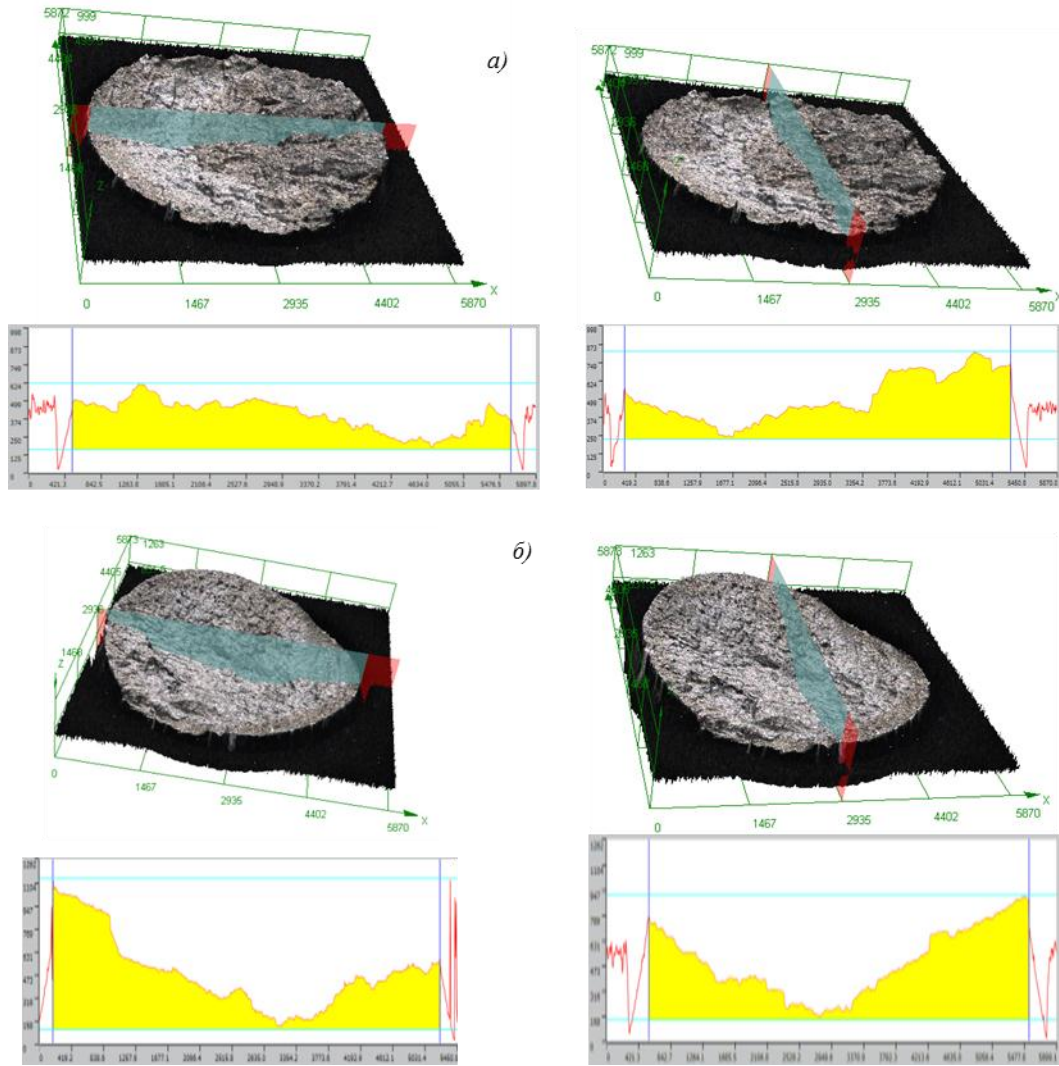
Поверхности и рельефы разрушения двух галтелей образца 3 – левой (а) и правой (б)
